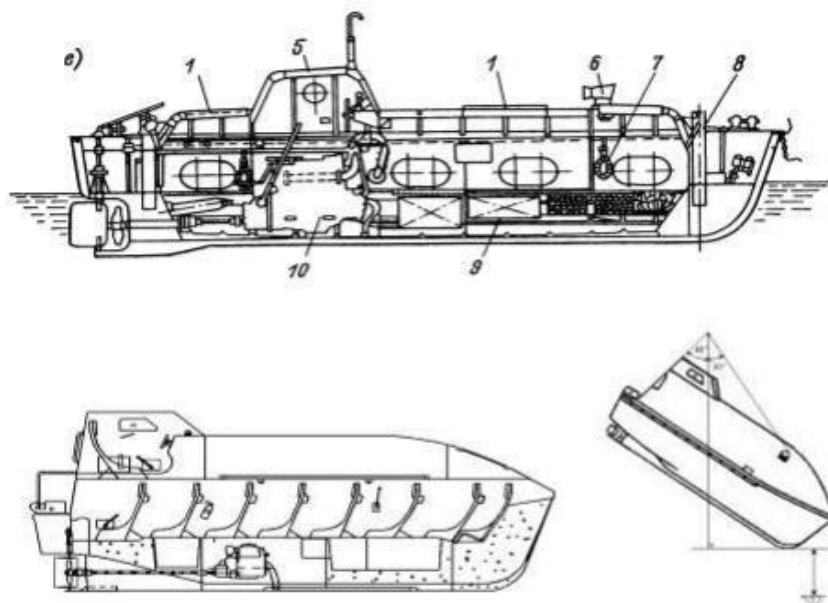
Разрез закрытой спасательной шлюпки, ж – сбрасываемая шлюпка: 1 – крышки; 2 – люк сходный; 3 – люк световой; 4 – леер спасательный; 5 – рубка рулевая; 6 – вентиляционная головка; 7 – бросательный конец; 8 – подъемное устройство; 9 – рундук; 10 – двигатель.
